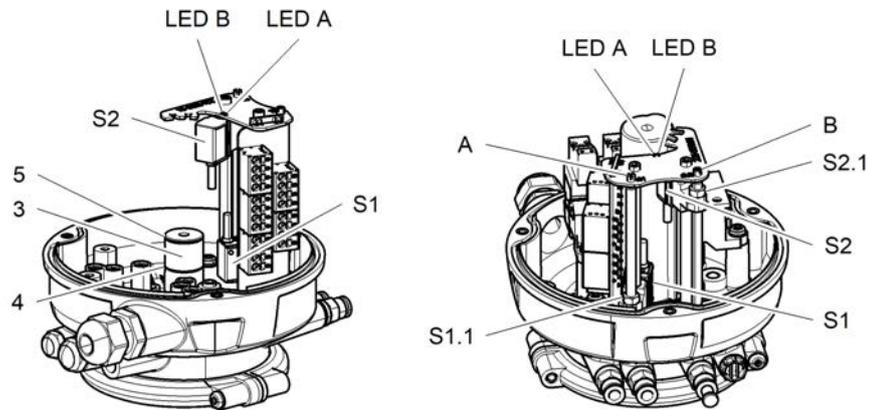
Steuerkopf ohne Pneumatikblock dargestellt
